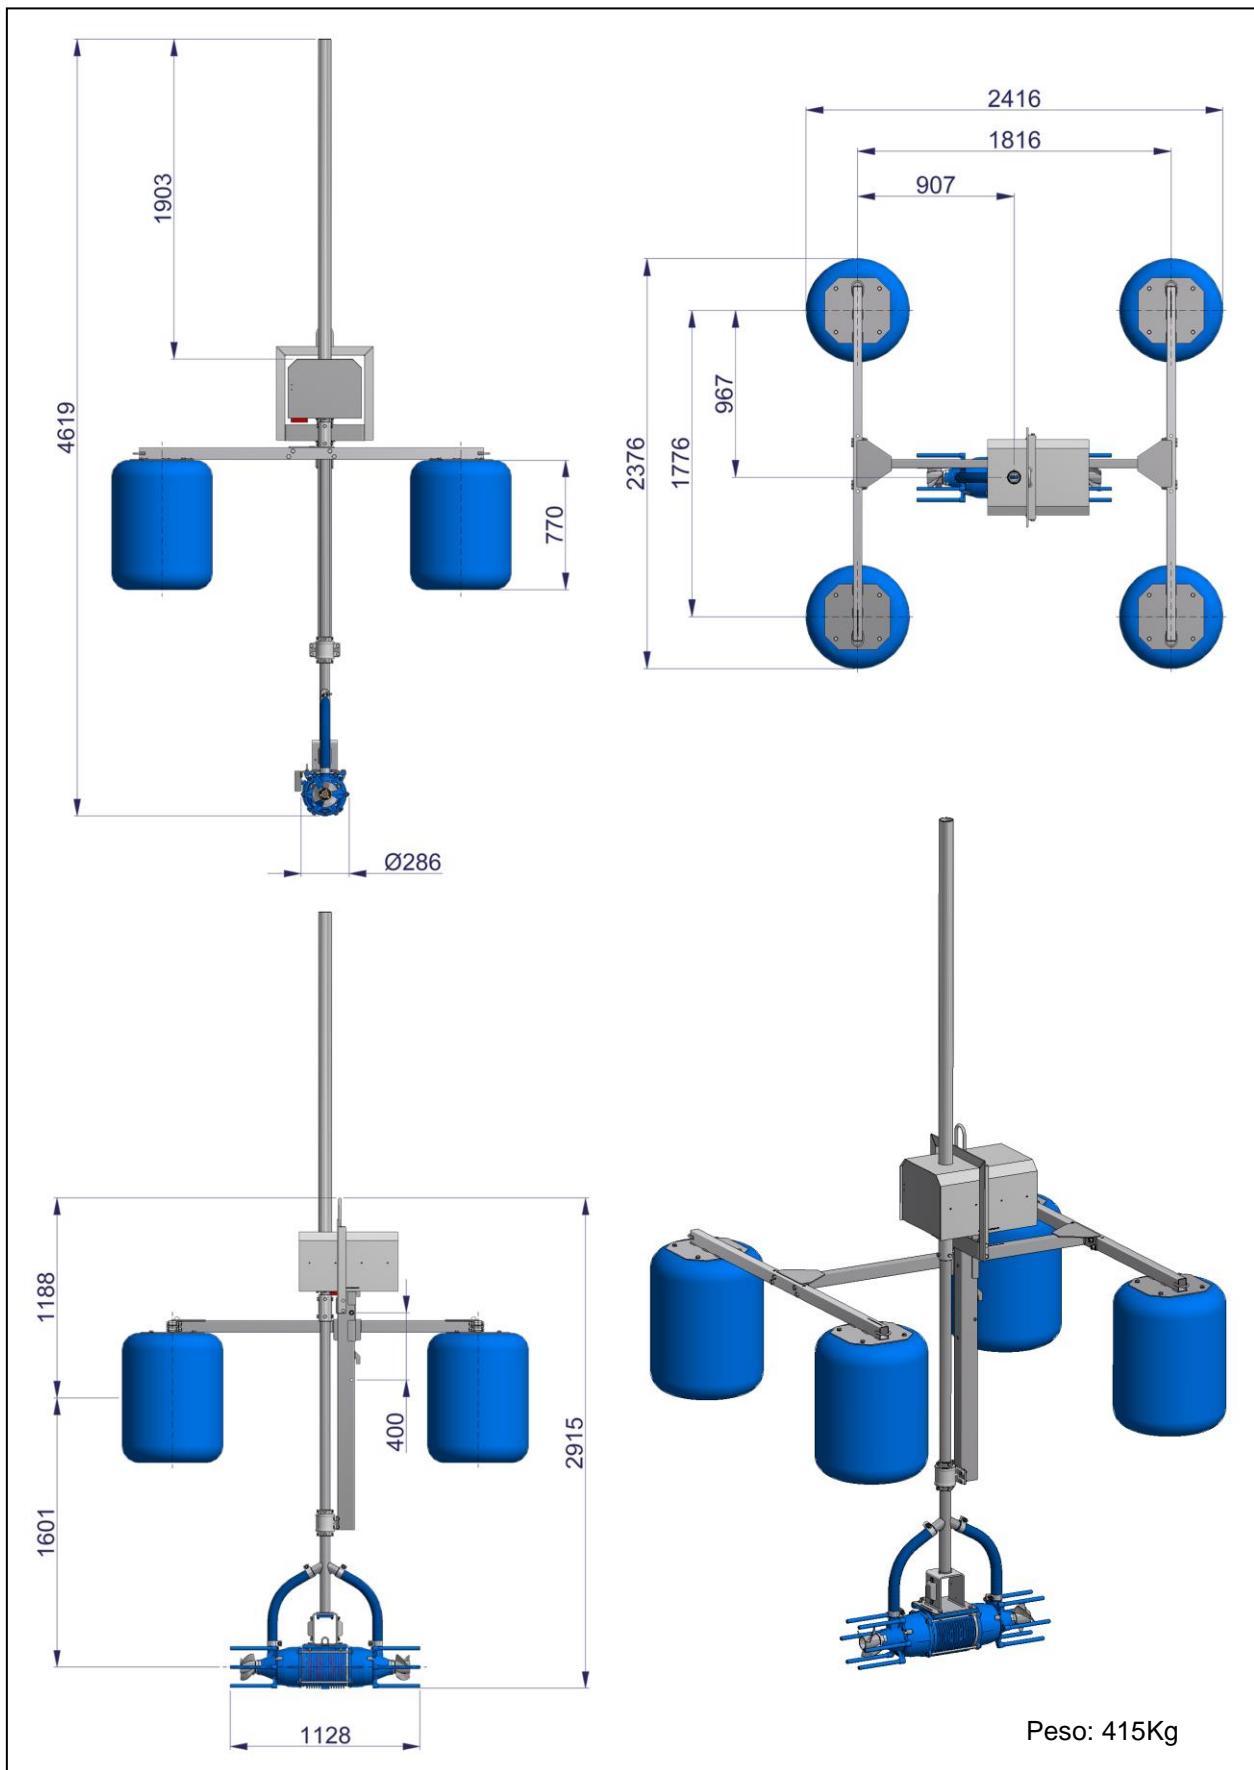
Dimensional TORNADO-R BITURBO 10, 12,5, 15 e 20CV
